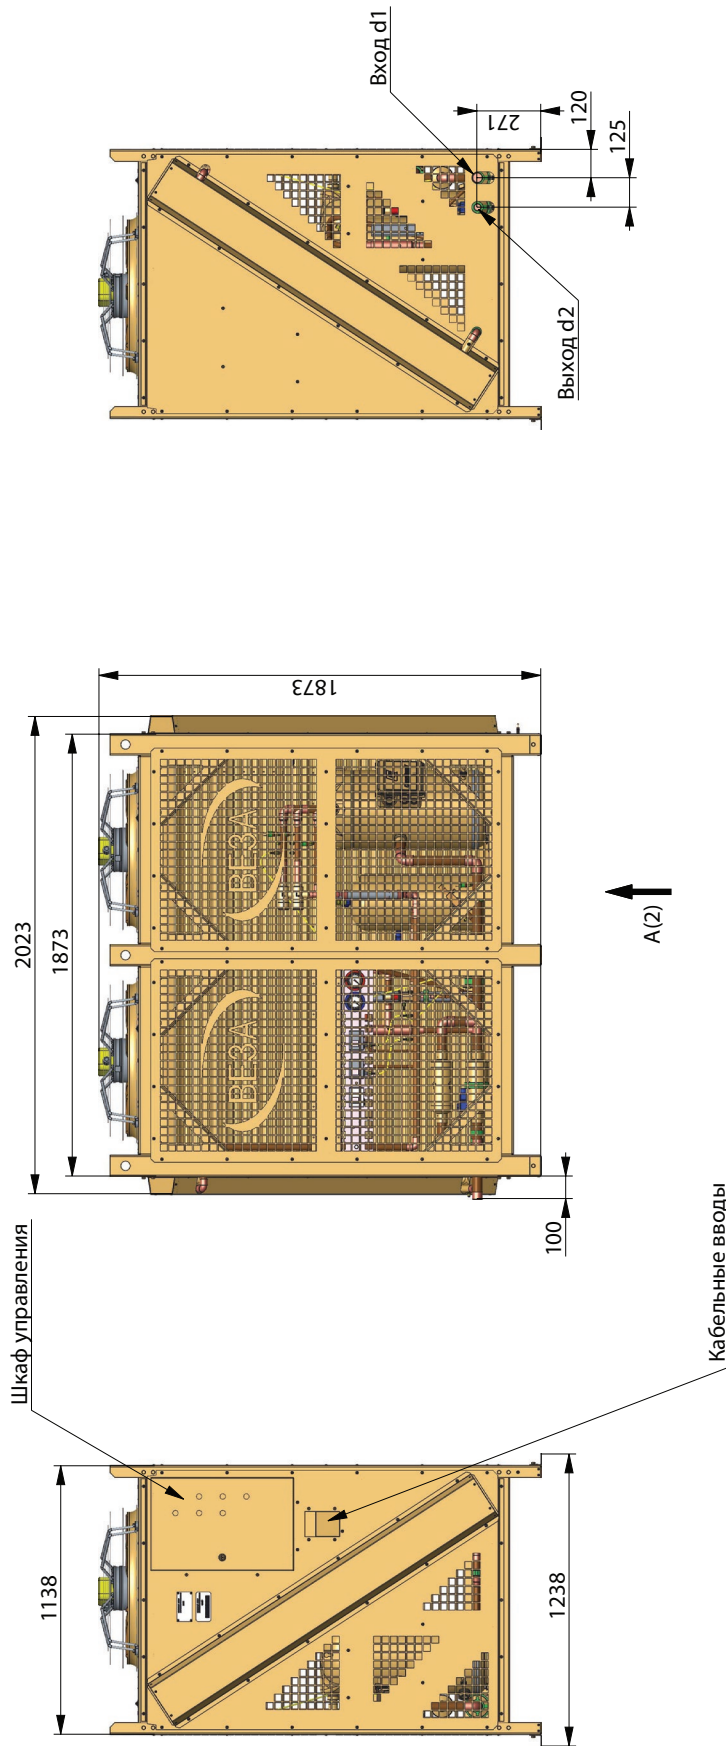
Агрегат компрессорный МАКК 120-621, -781
